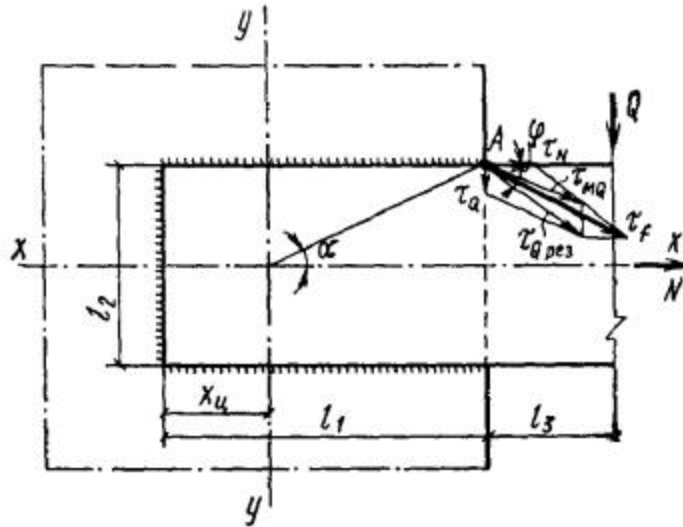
К расчету сварного соединения с угловыми швами на одновременное действие продольной и поперечной сил
